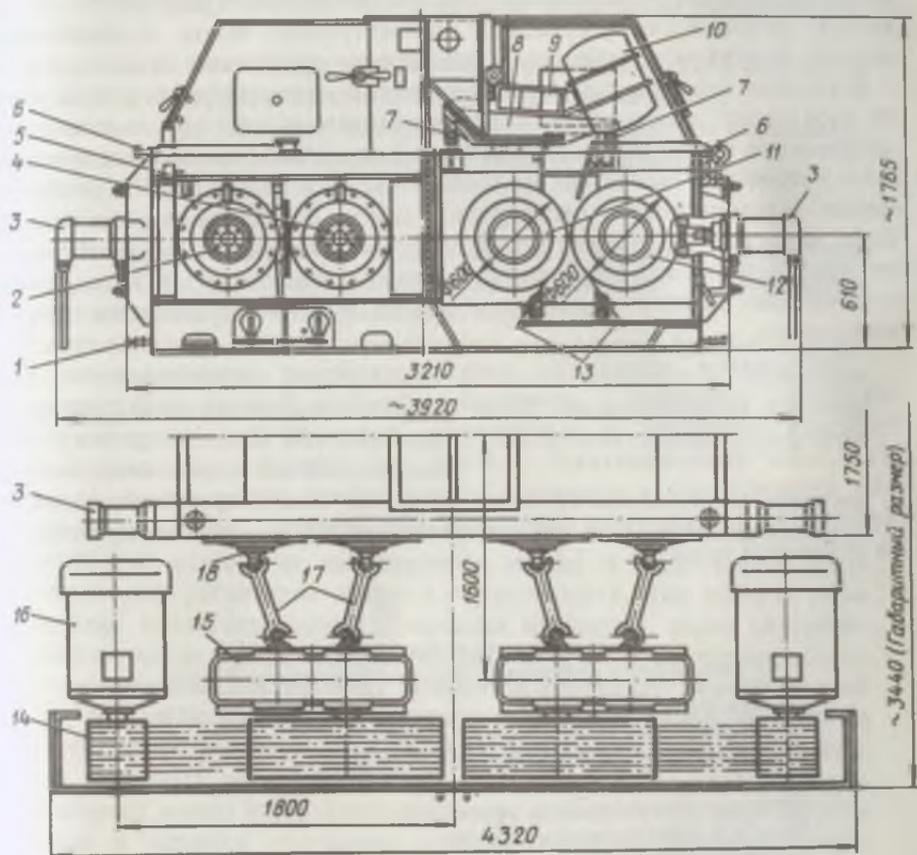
Двухпарный плющильный вальцовый станок ФВ-600 (ФРГ)
